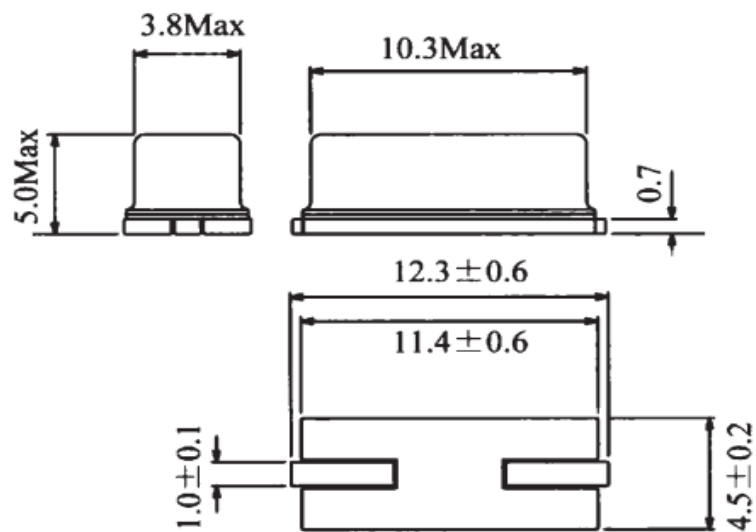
Габаритні розміри кварцового резонатора HS-49SM
